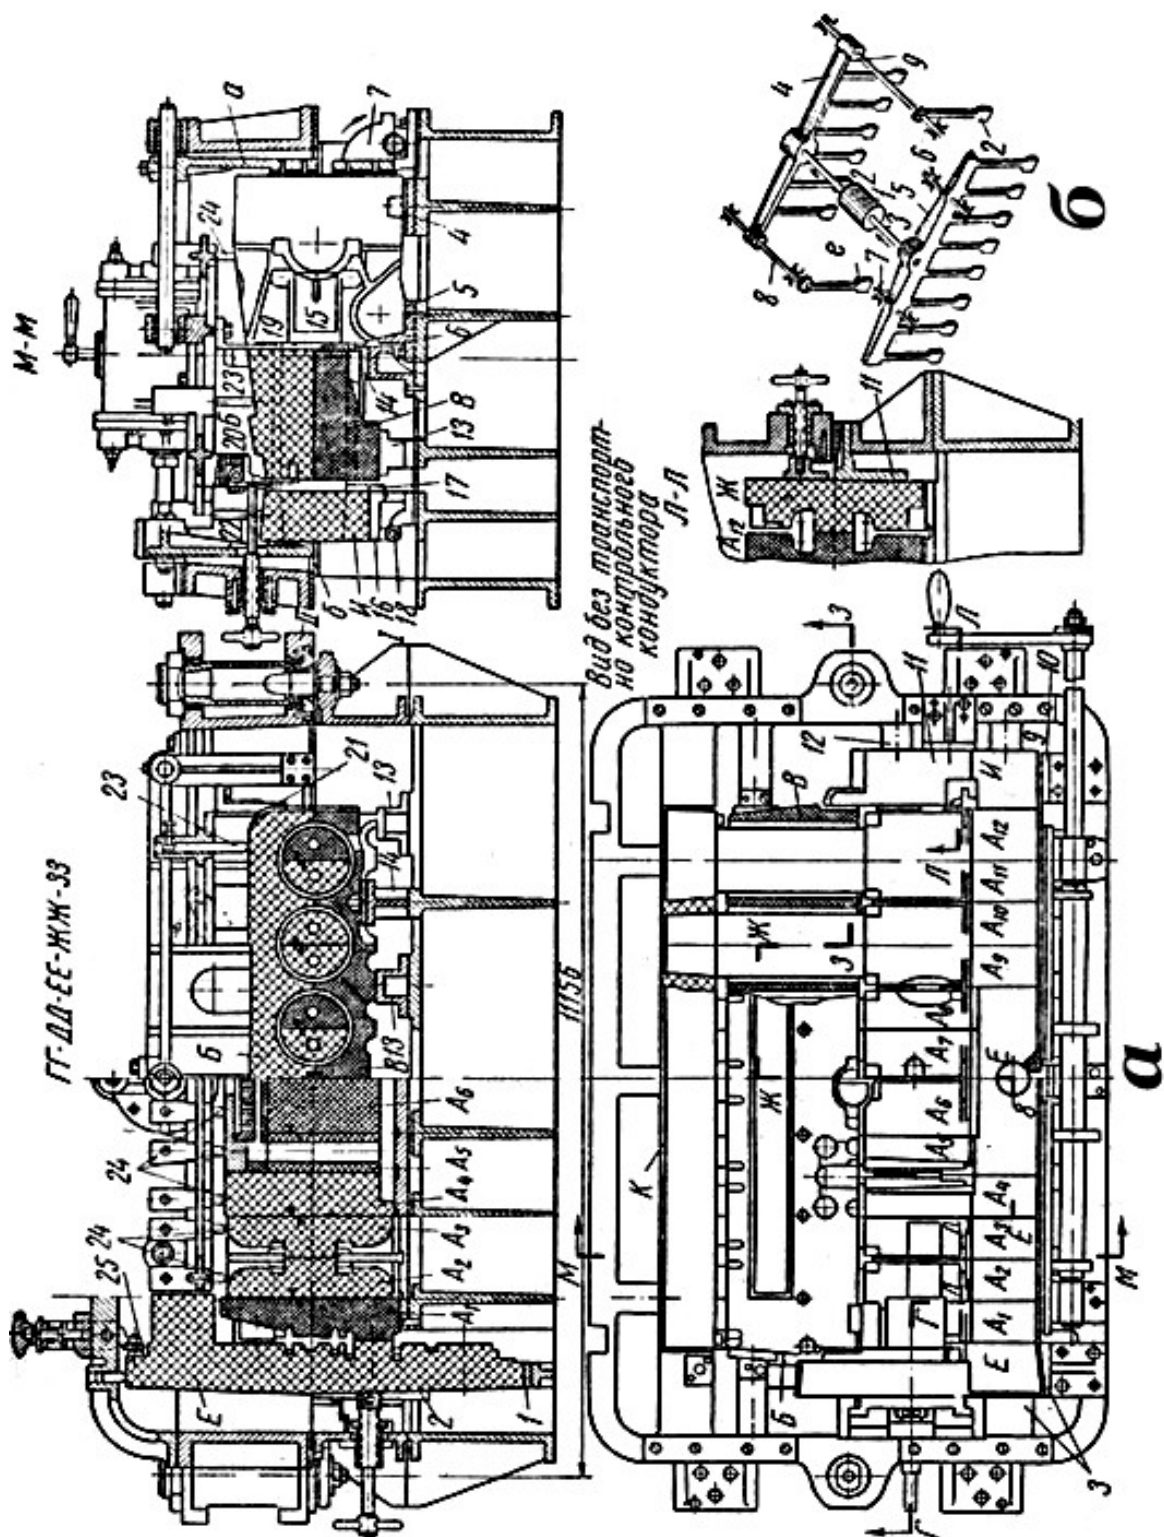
Сборка стержней отливки блока цилиндров автомобильного двигателя: а – сборка стержней блока цилиндров в кондукторе; б – кинематическая схема контрольно-транспортного кондуктора
